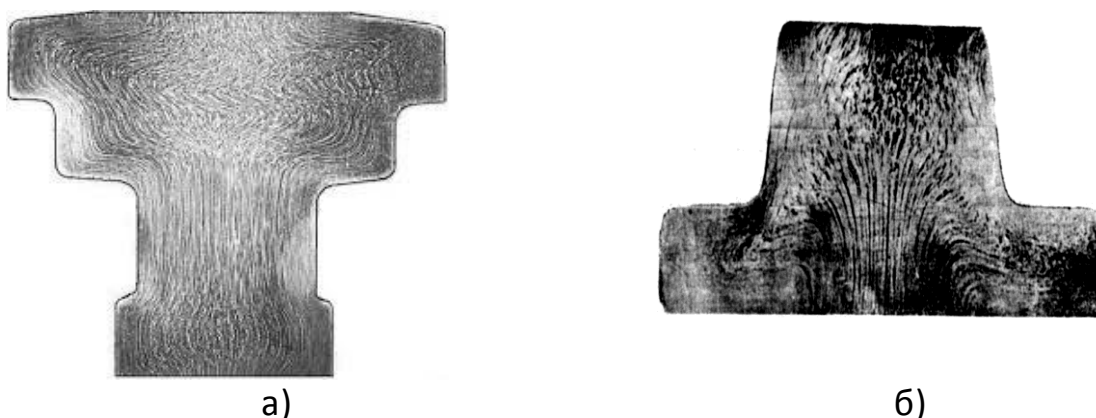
Макроструктура стальных заготовок для шестерен:
